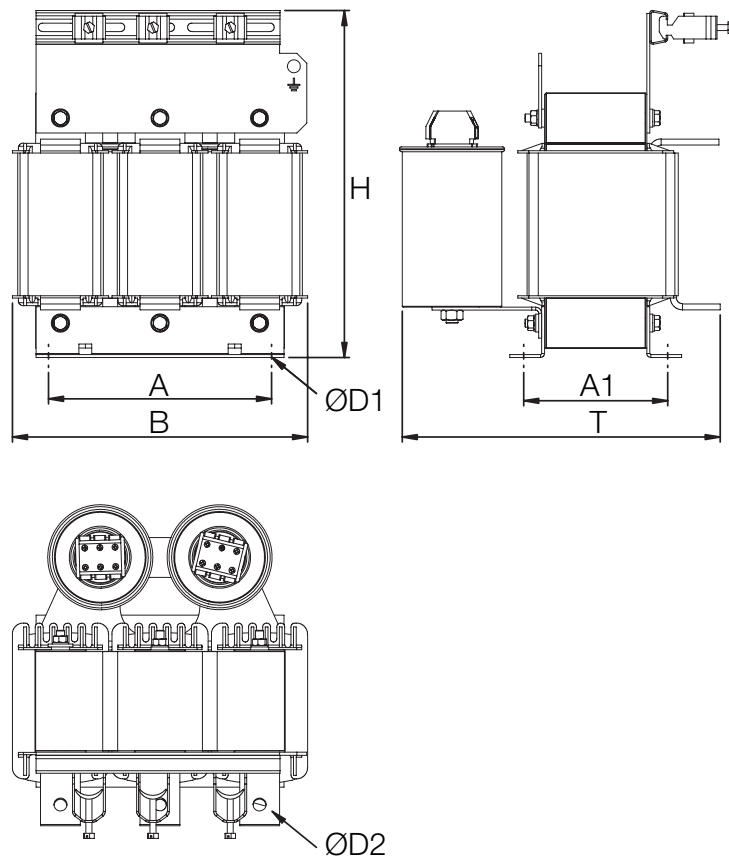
Maßzeichnung Vordrossel beispielhaft für BG7 (G396-250)
